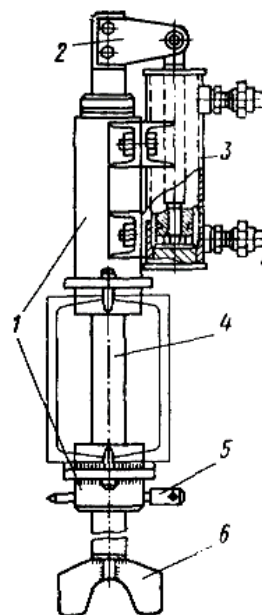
Прижим с гидроцилиндром, установленный на ложементе:
